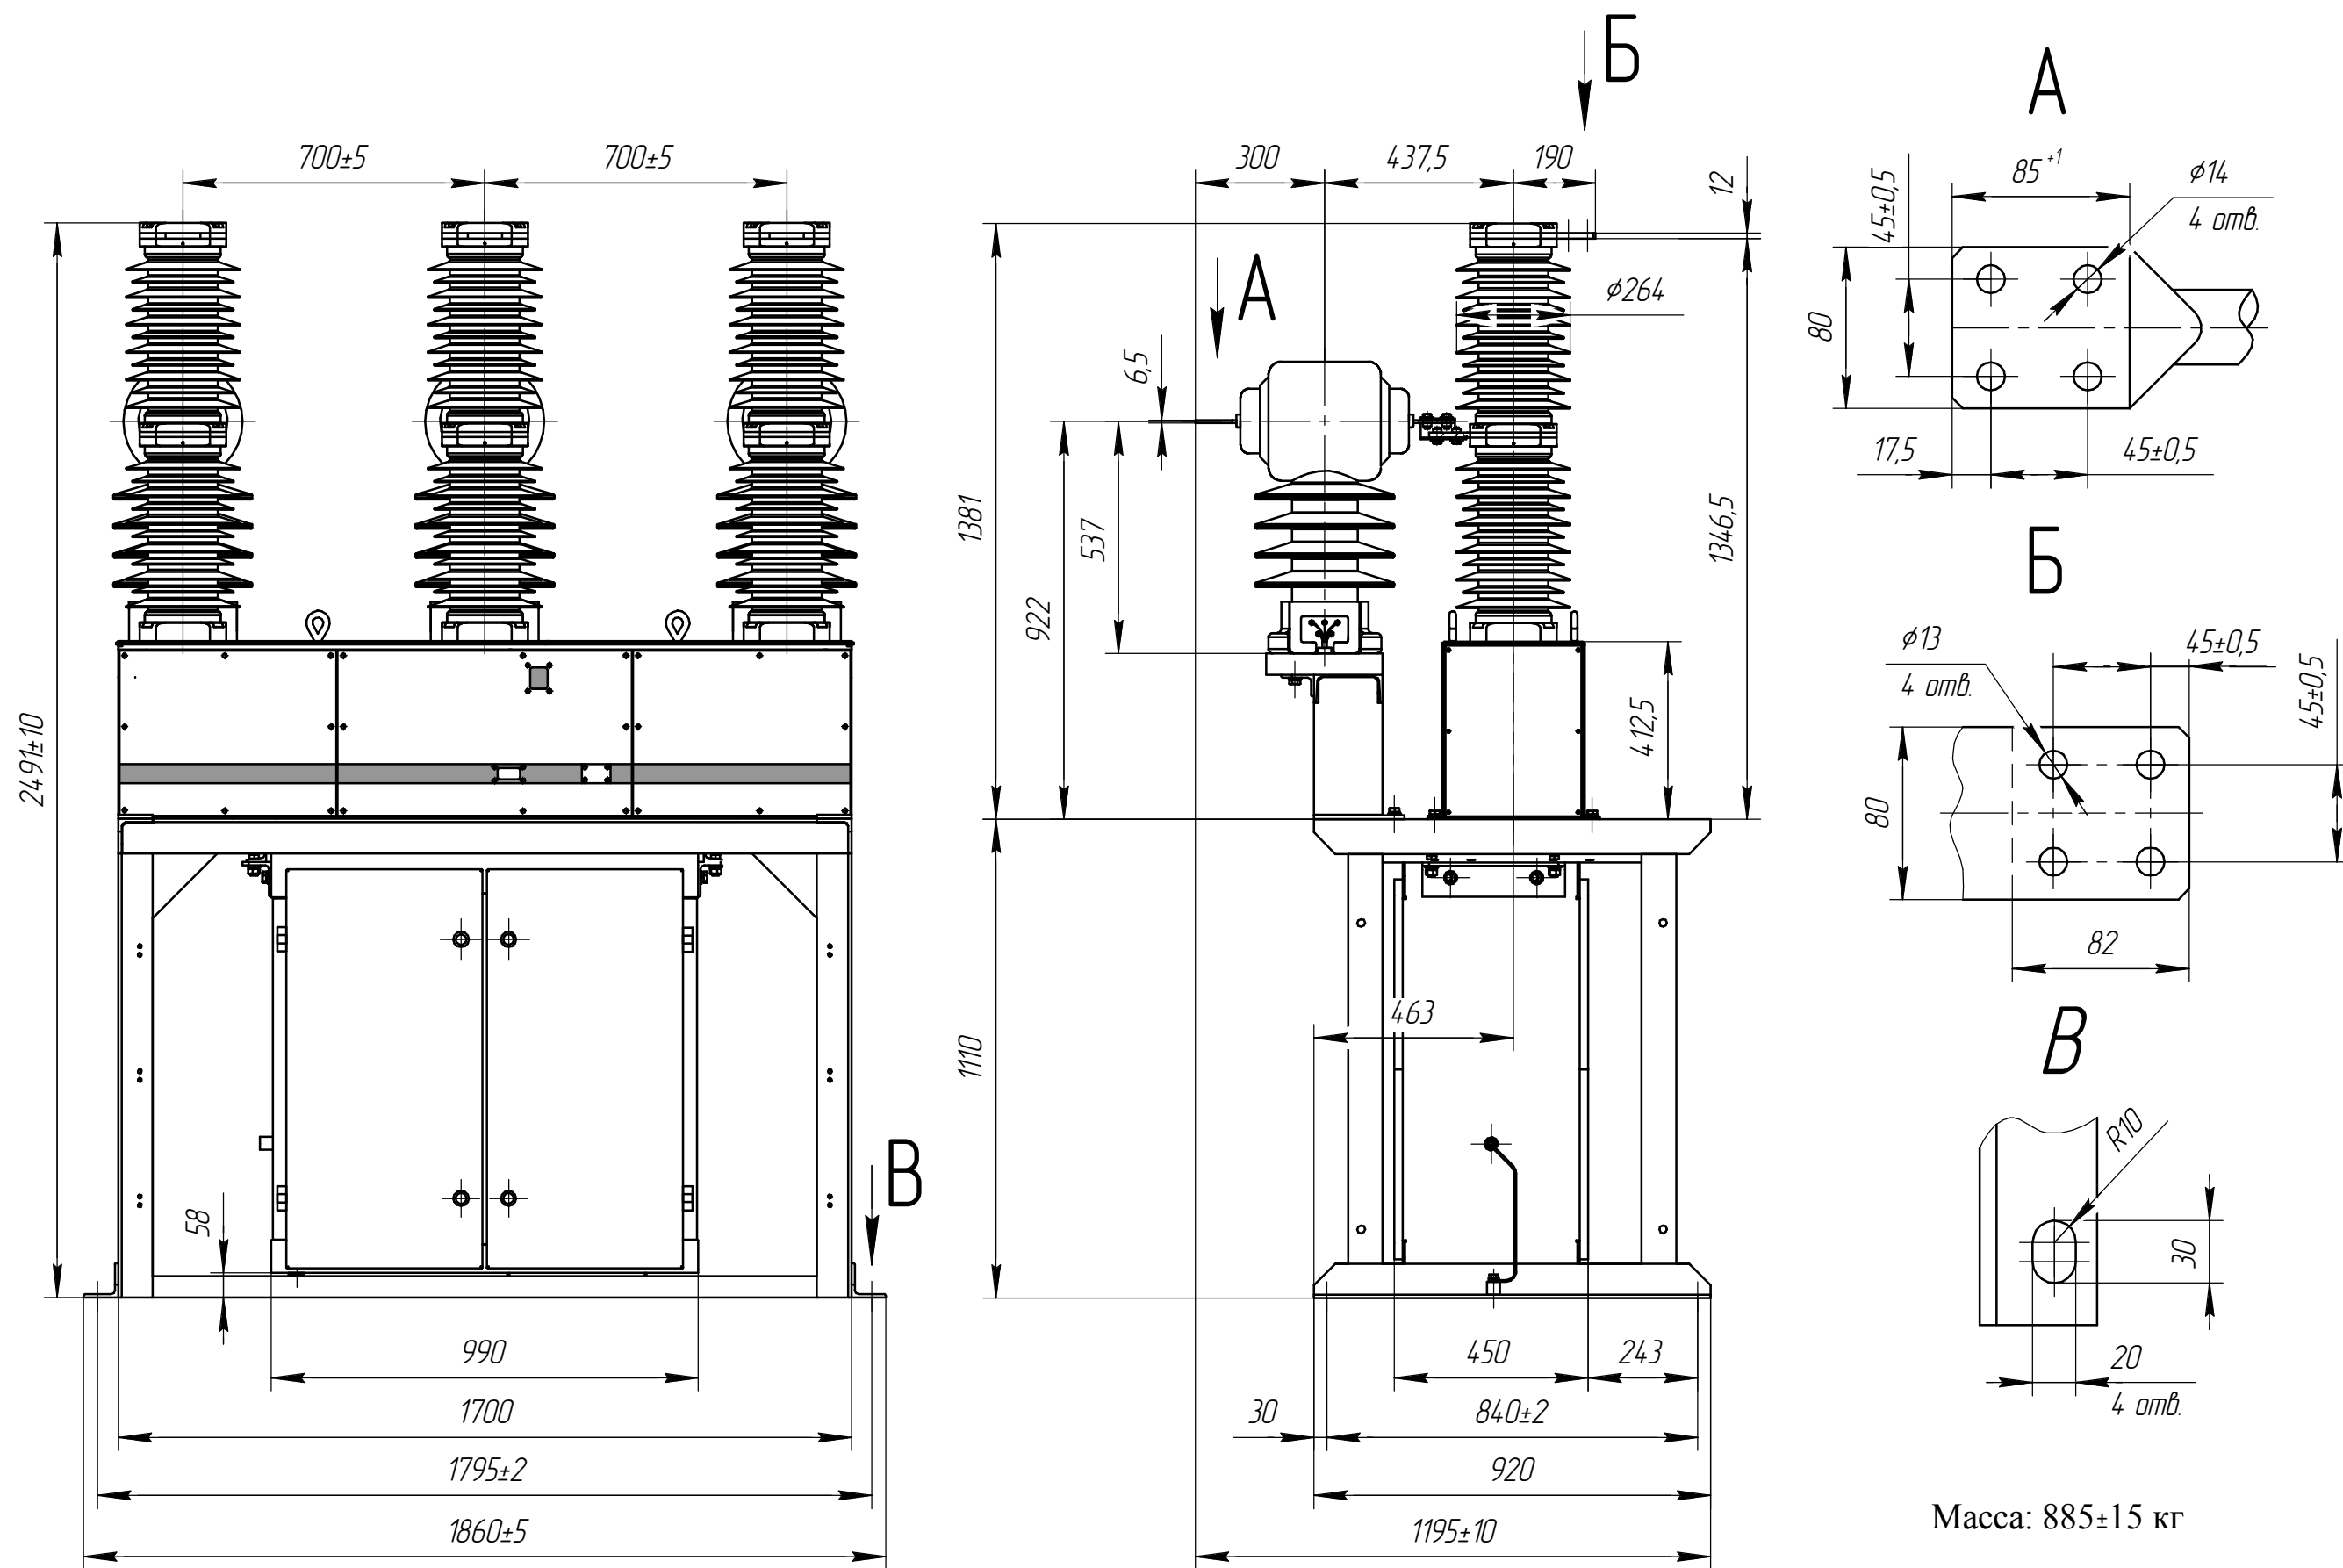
Габаритные, установочные и присоединительные размеры выключателя типоразмера ВР35НТ-35-25/1600-3/0 УХЛ1 с тремя встроенными трансформаторами тока ТОЛ-35 III-IV-1; 3; 5; 7 УХЛ1 со стороны нижних контактов
